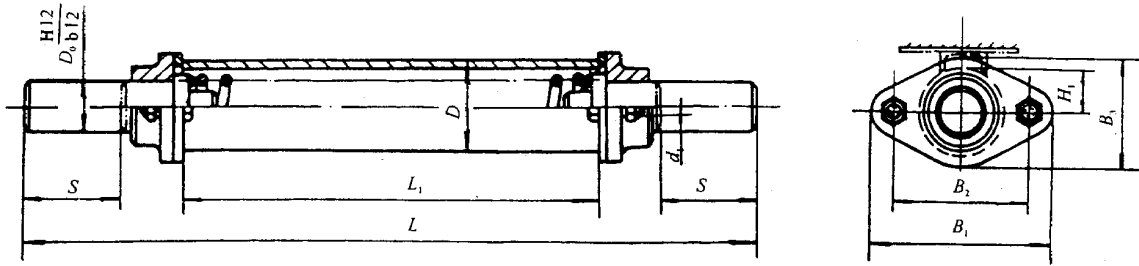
HT1 型壳体焊接式弹簧缓冲器
